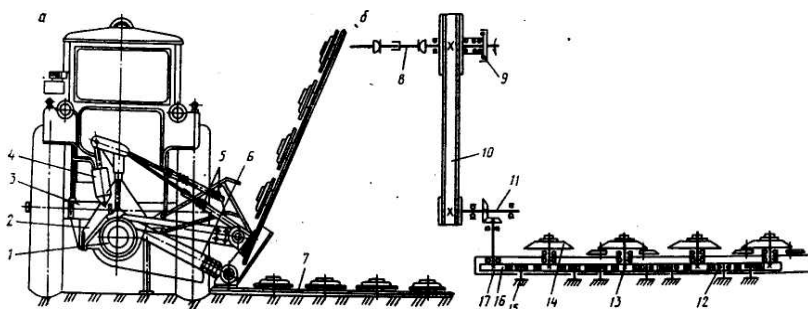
Общий вид и кинематическая схема четырехроторной косилки:
